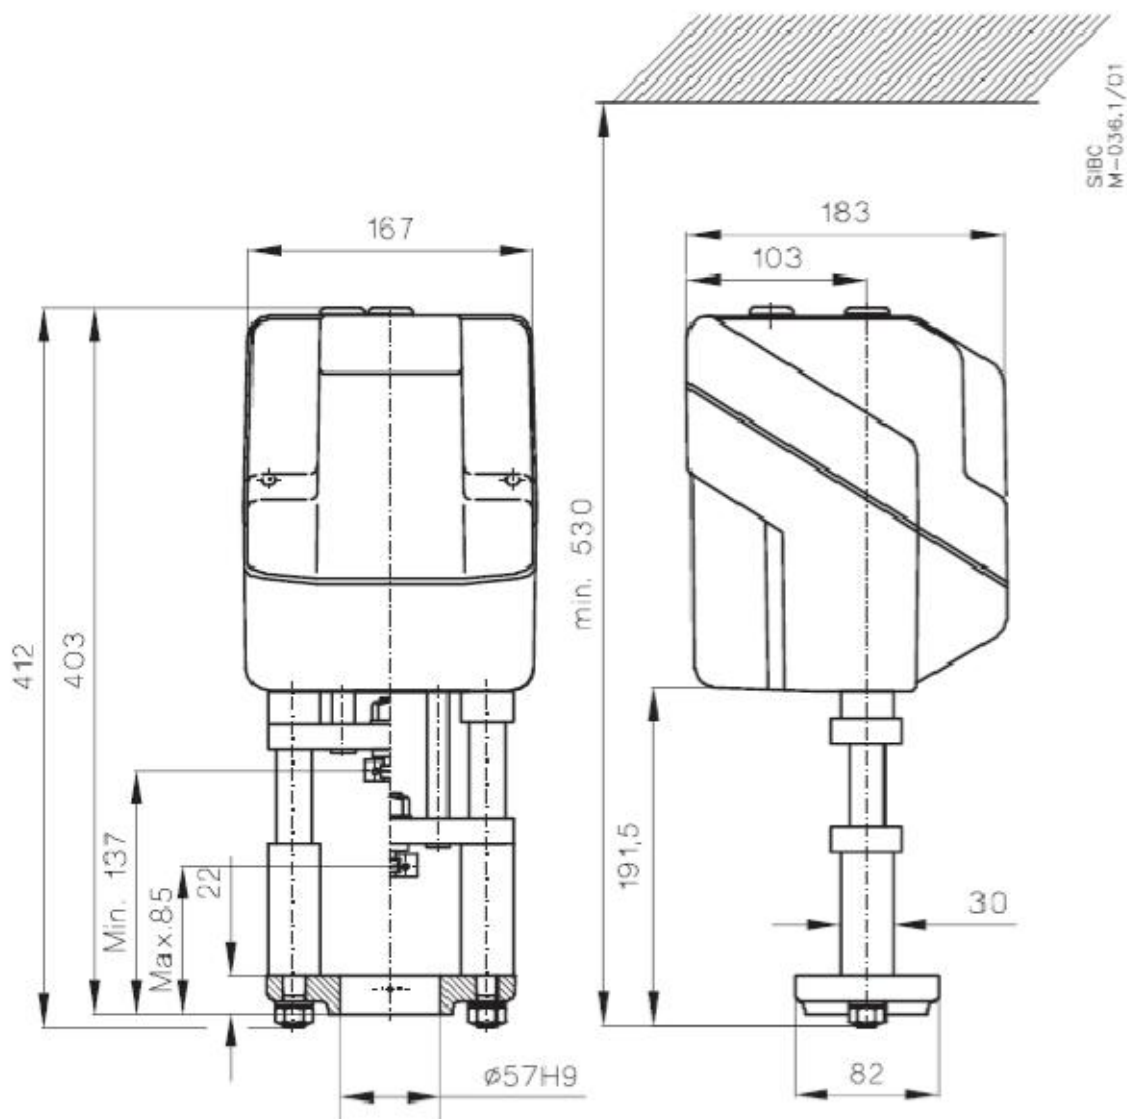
Габаритные и присоединительные размеры AME 10, 20, 30, 13, 23, 33.
